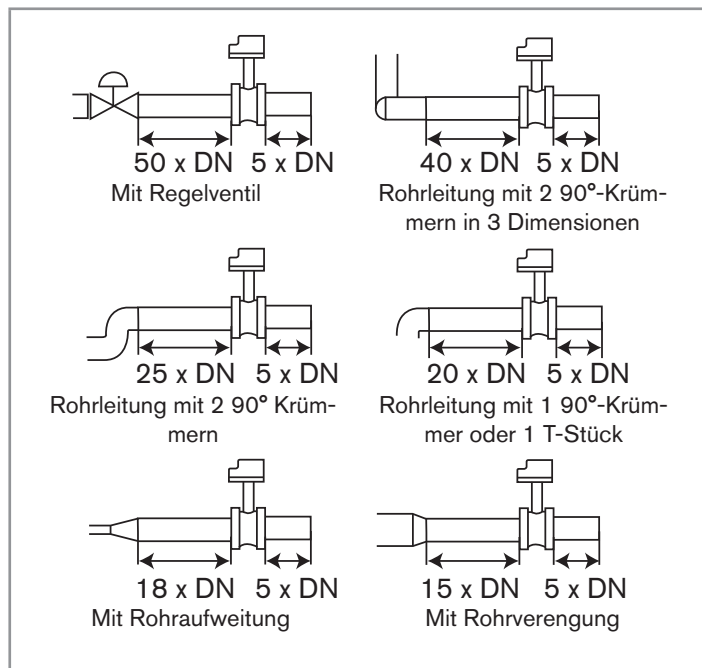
Mindest-Ein- und -Auslaufstrecken je nach Aufbau der Rohrleitungen.
